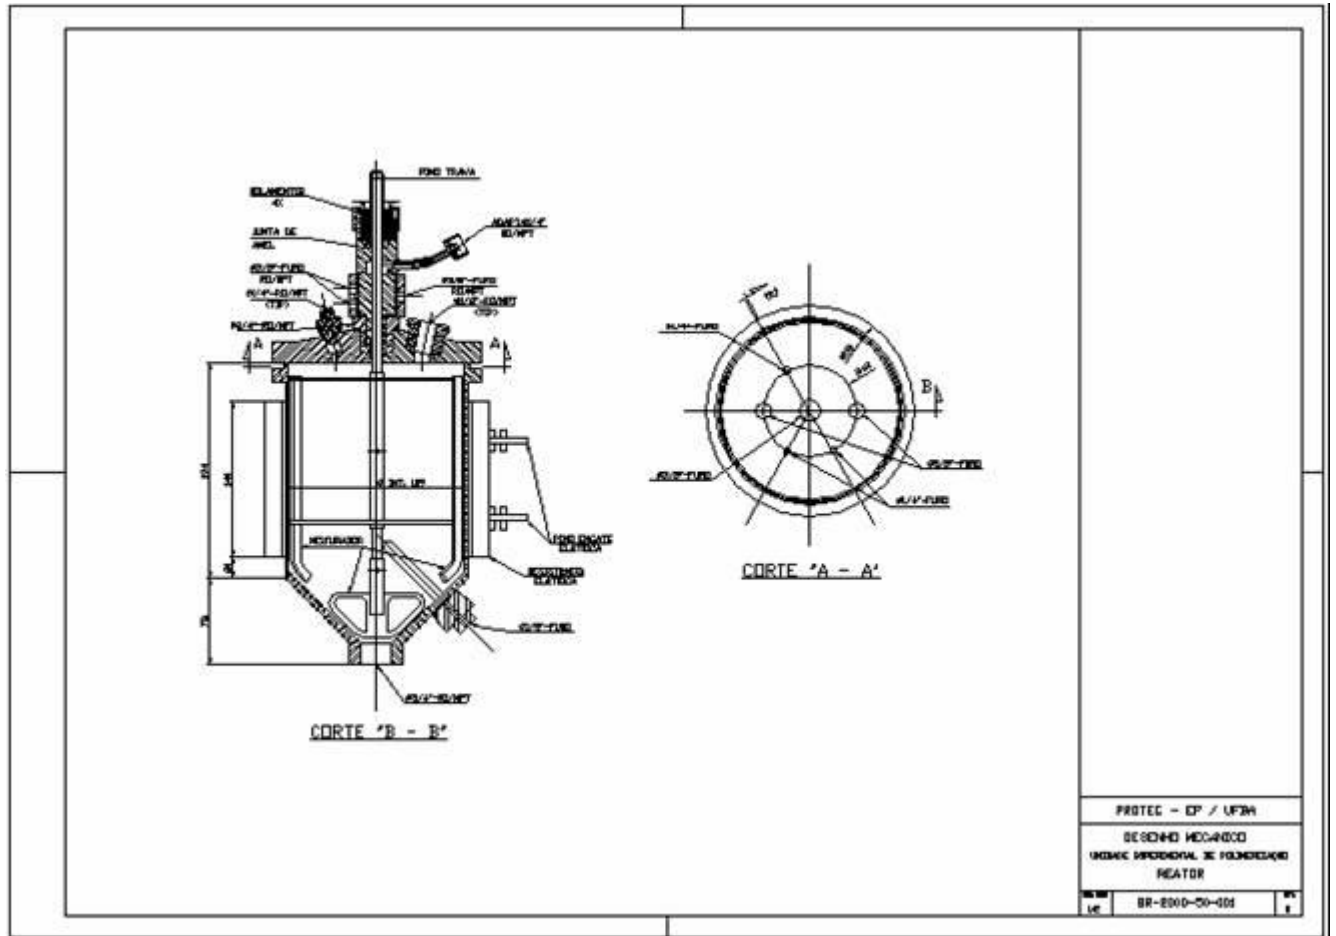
Desenho Mecânico do Reator com Detalhes e Cortes.
